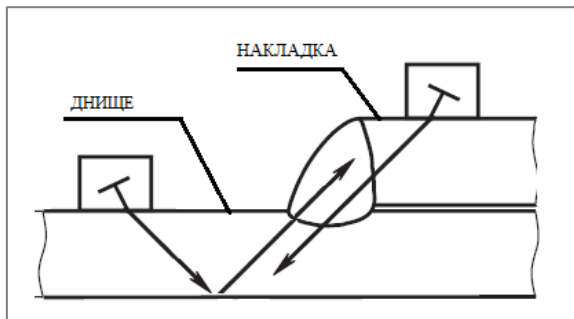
Схема контроля нахлесточных сварных соединений.
